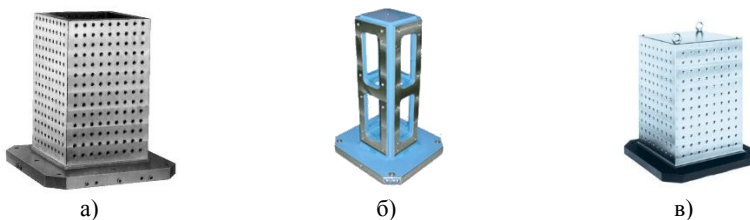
Конструкції колон: а – твердотільна; б – рамна; в – зварювальна
